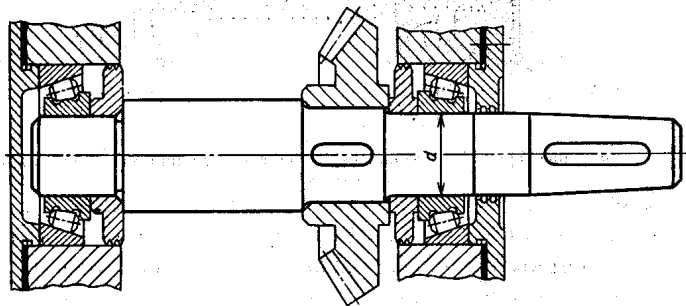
Вал конического редуктора установлен на конических роликоподшипниках, поставленных враспор
